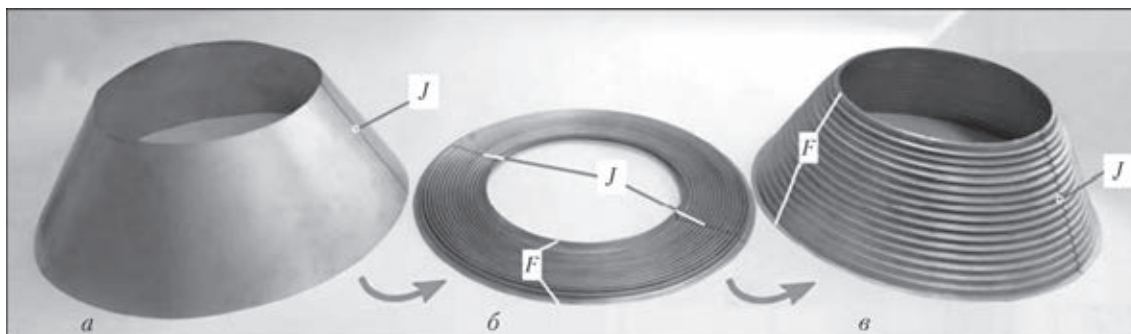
Стадии изготовления преобразуемой конической оболочки КПО, иллюстрирующие характер технологического деформирования ее сварных соединений J (F — фланцевая отбортовка для последующей сварки оболочек в единую структуру)
